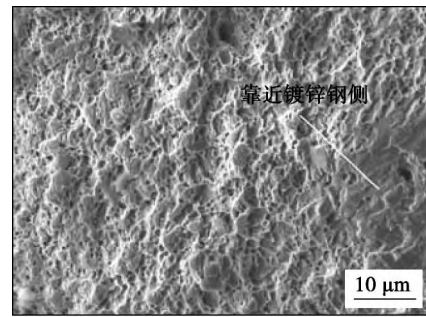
接头拉伸断口形貌(焊缝处断裂)
